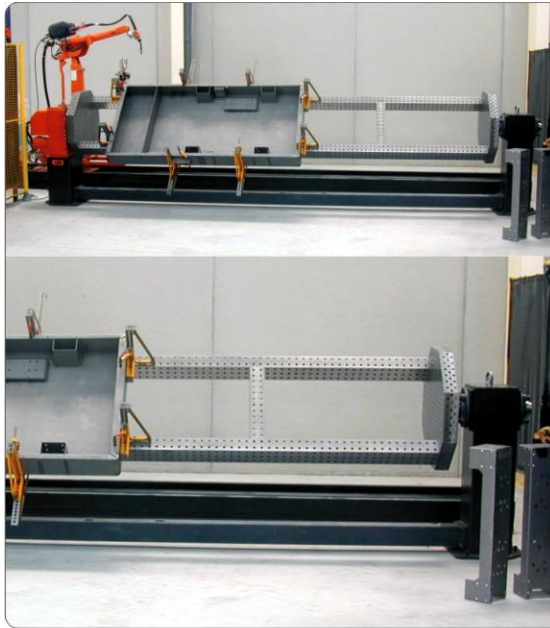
Tabla de altura de elevación de soldadura de montaje MSE-08-02 hidráulica regulable.³⁴
